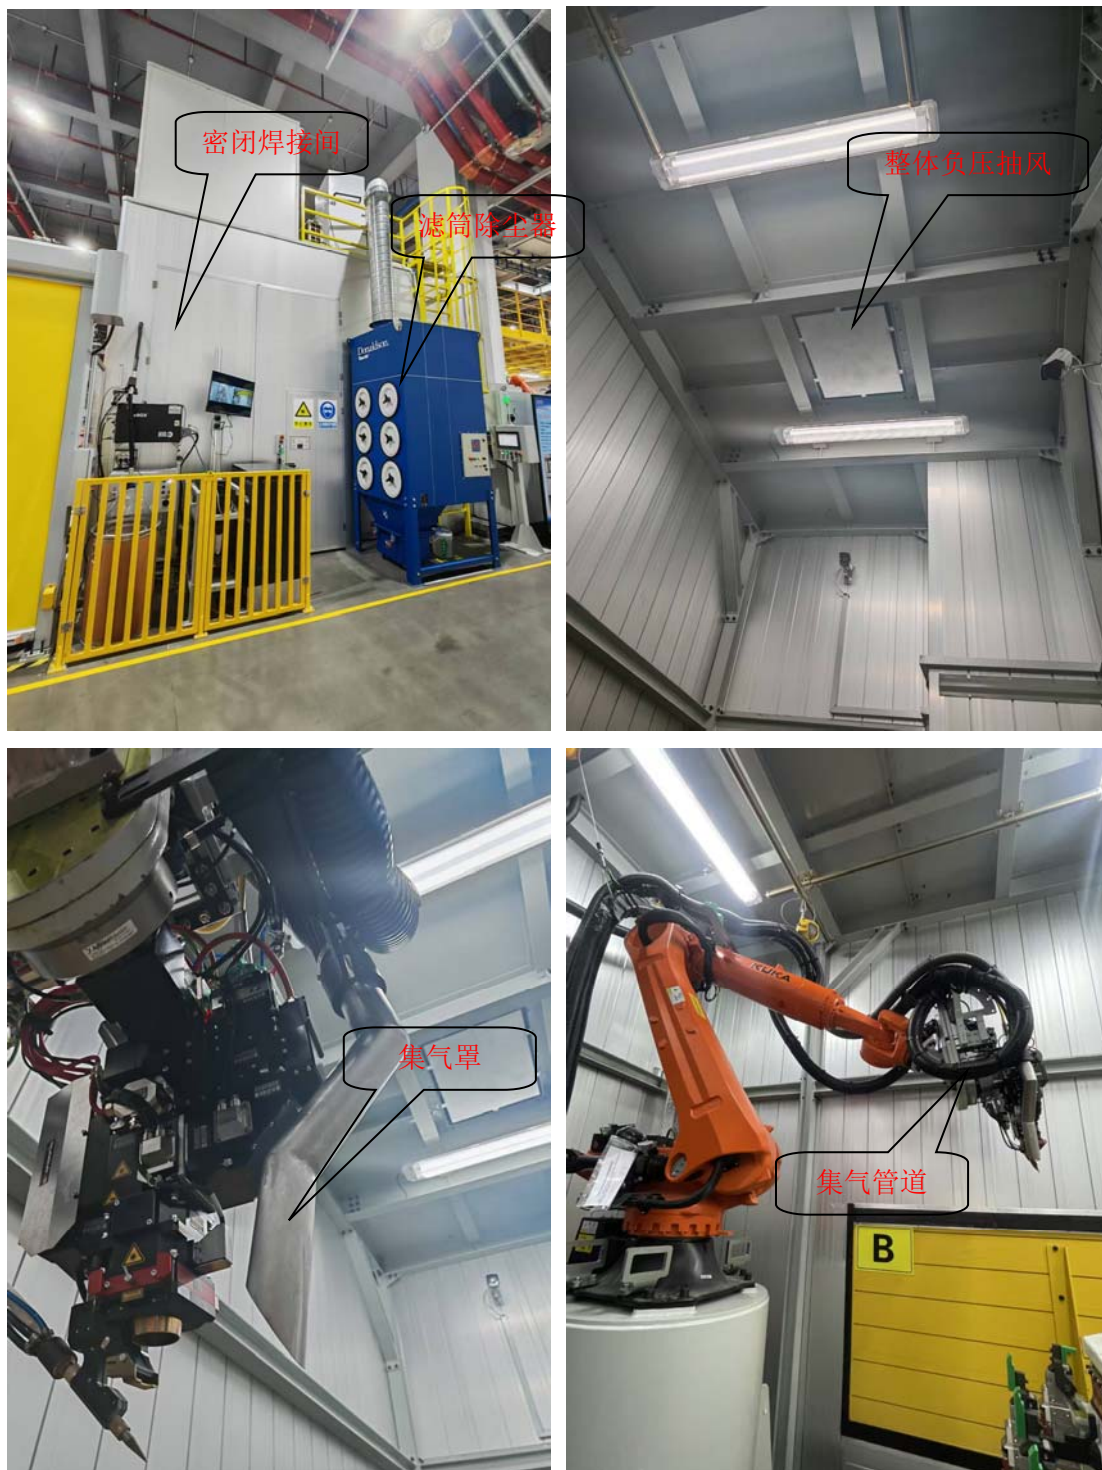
焊接平台所在的焊接间以及废气收集图片
